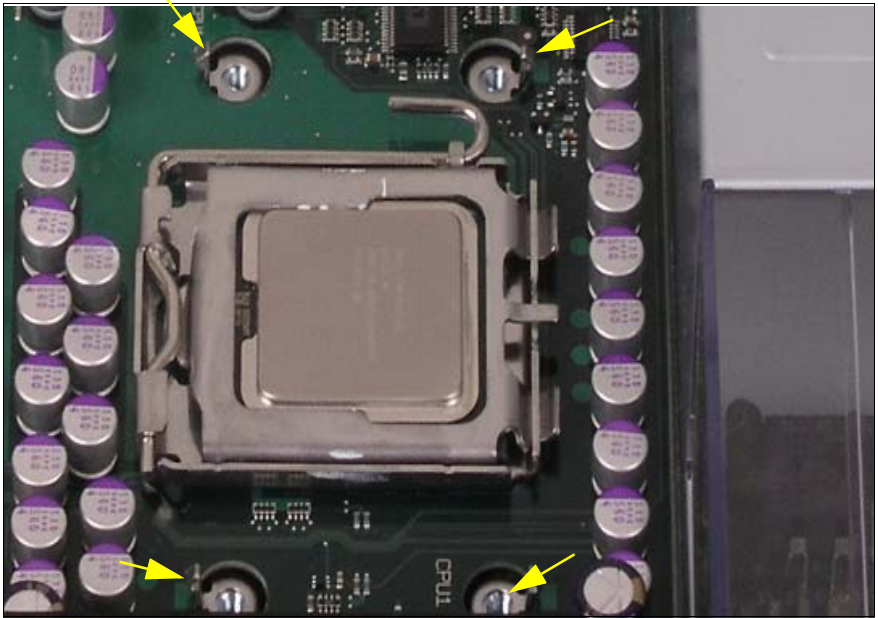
Federn auf den Kühlkörperhaltebolzen beachten
